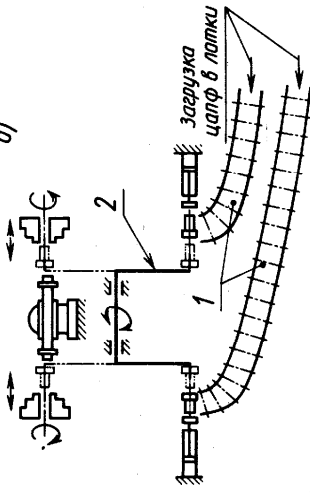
Схема автоматической установки для сборки и сварки корпуса картера с цапфами
